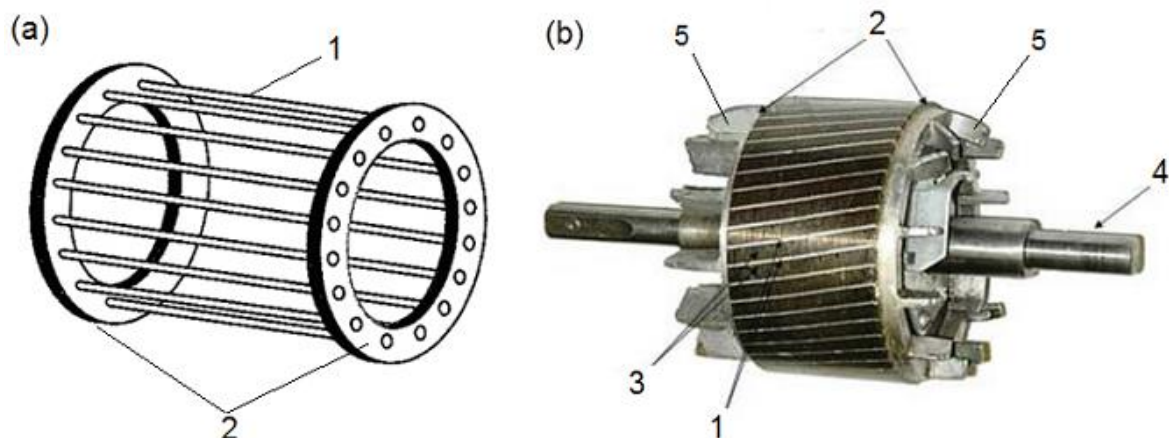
Rotor à cage d'écureuil : 1- Barre du rotor, 2- Bague d'extrémité du rotor, 3- Noyau du rotor, 4- Arbre, 5- Pales du ventilateur de refroidissement.
